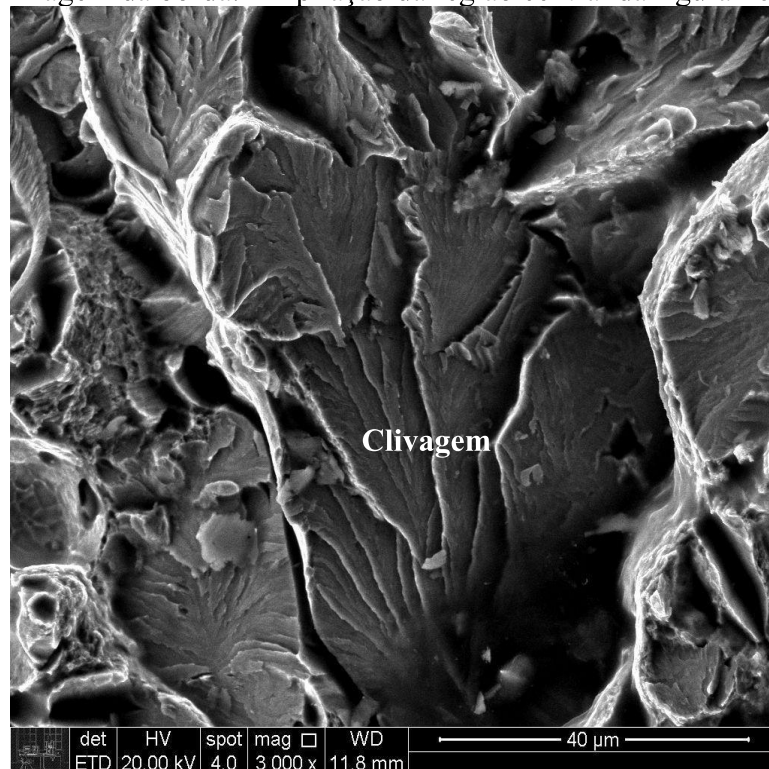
Imagem obtida por MEV da superfície de fratura do corpo de prova da solda S16.
